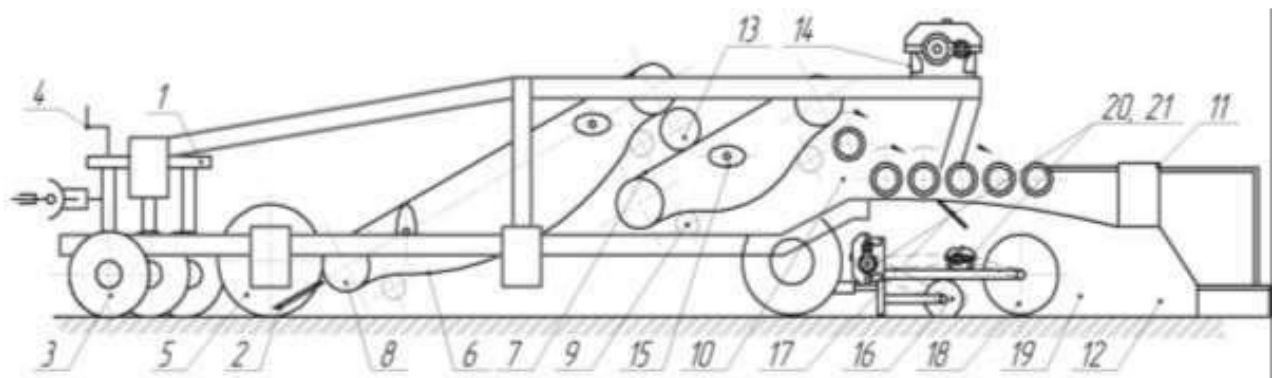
Конструктивно-технологічна схема машини для збирання цибулі-сіянки: 1 – рама; 2 – леміш; 3 – колеса ходові; 4 – механізм регулювання глибини підкопування; 5 – ніж дисковий; 6, 7 – основний і допоміжний сепарувальні елементи; 8, 9 – ботвопротягувальний і підтримувальний ролик; 10 – роликовий сепаратор; 11 – лоток звужувальний; 12 – утворювач валка; 13 – ботвоудаляювач; 14 – редуктор; 15 – струшувачі еліптичні; 16 – рама котка-ложеутворювача; 17 – лоток сходження домішок; 18, 19 – спіральний і циліндричні вальці; 20, 21 – гідромотори приводу вальців котка-ложеутворювача.
